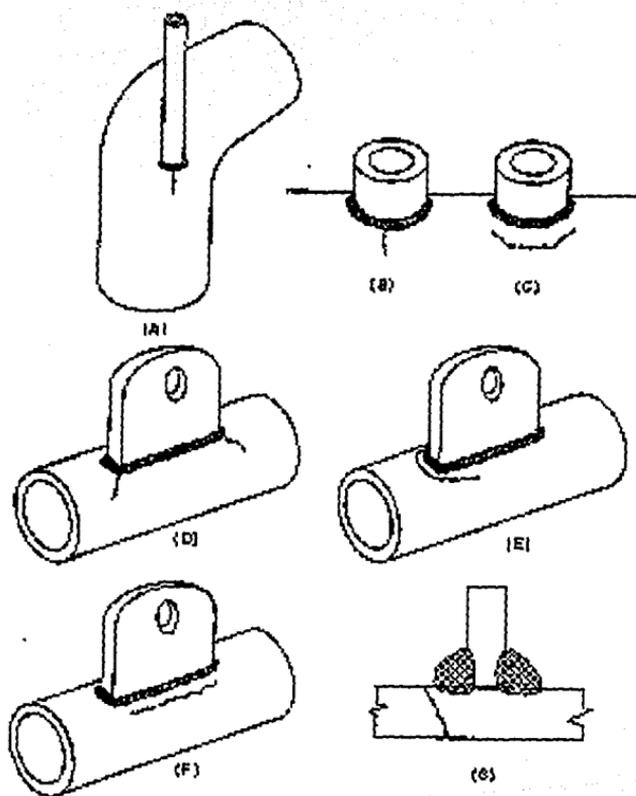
Ejemplos de grietas debidas a esfuerzos por corrosión y fatiga por corrosión en soldaduras de injertos y elementos de sujeción de tuberías o depósitos.
